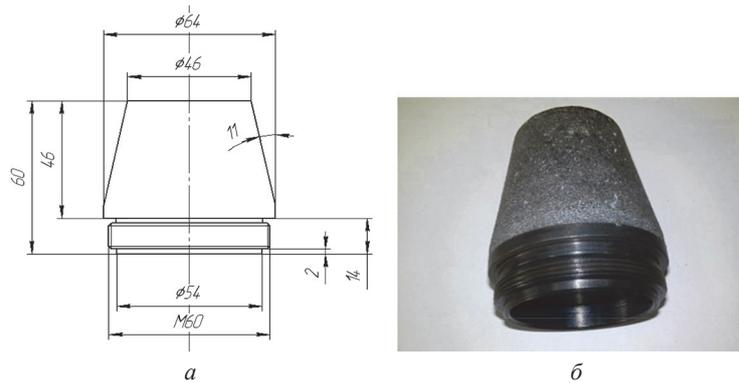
Эскиз (а) и опытный образец катода-мишени (б)
